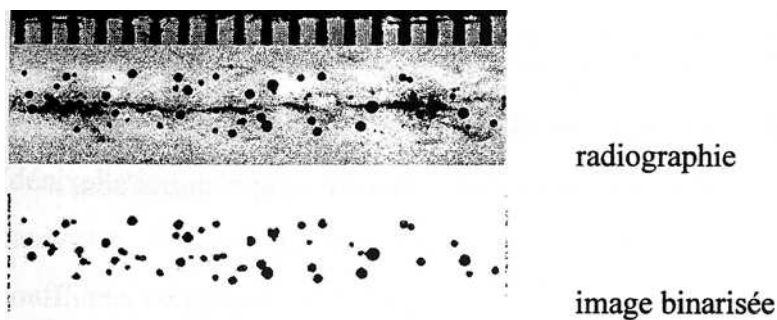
Porosité lors du soudage par laser CO₂ de tôles d'Al-Mg [Mayer].
